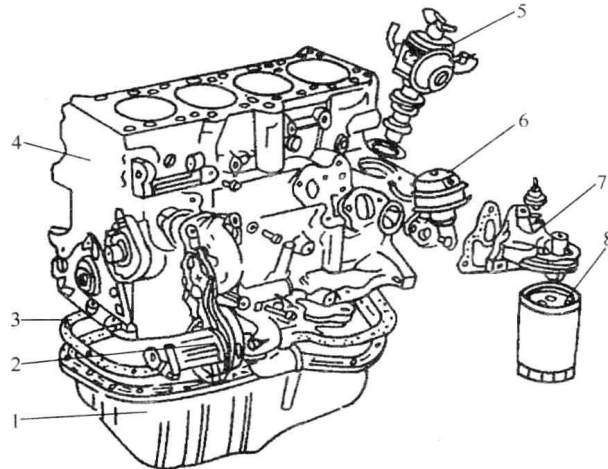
Main accessories of gasoline engine 汽油机的主要附件
